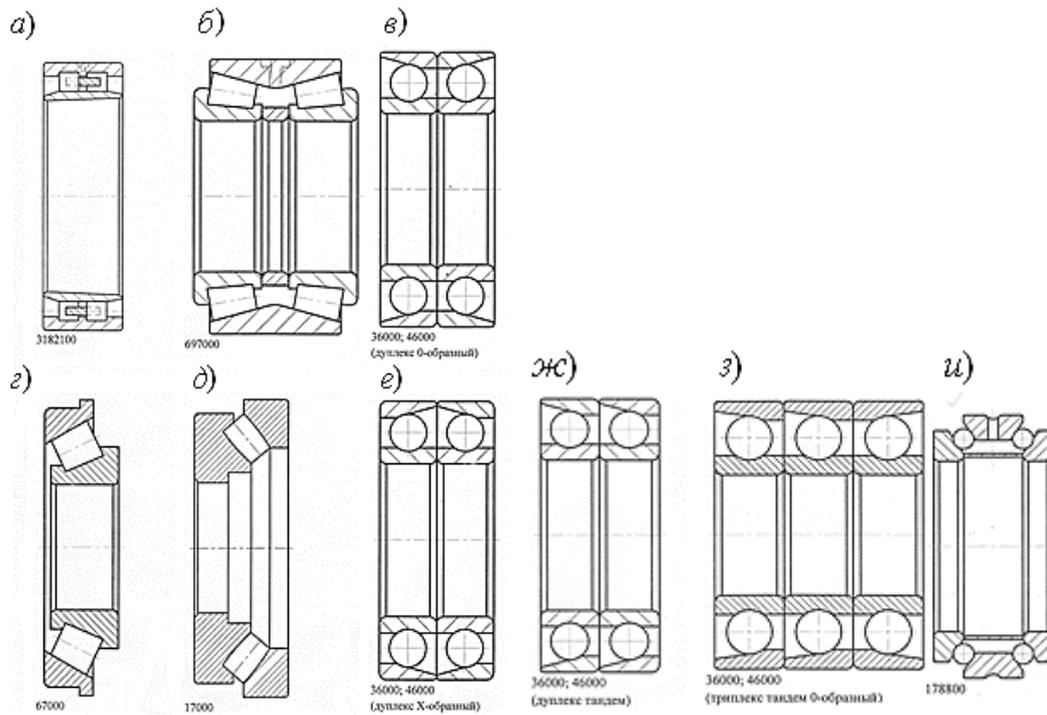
Типы подшипниковых опор шпиндельных узлов
